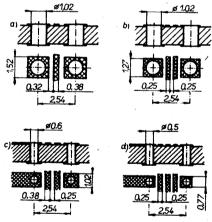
Tvary pájených spojů u základních součástek pro povrchovou montáž
